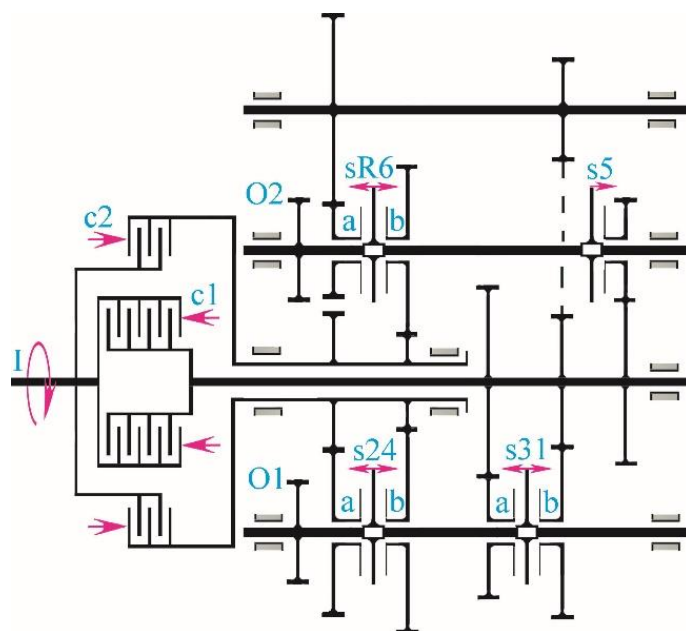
Кинематическая схема 6-ти ступенчатой коробки передач с двумя сцеплениями.
